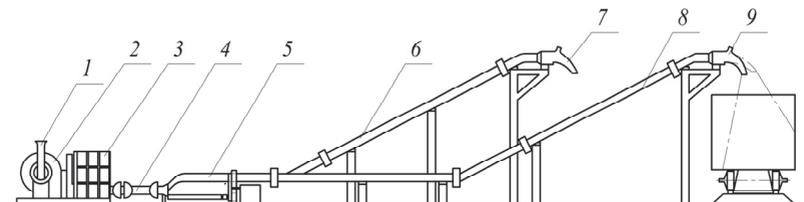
Пневмотранспортная установка ПНТУ-2М
